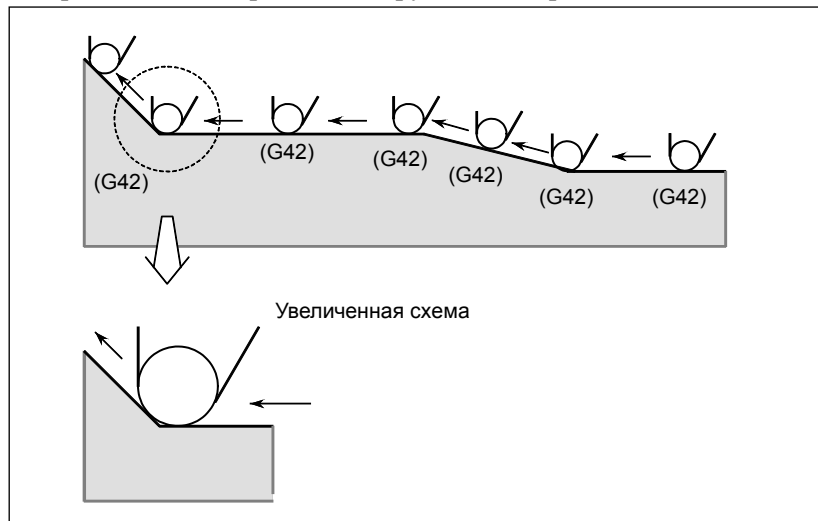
(с) Перемещение инструмента, если положение заготовки не изменяется
